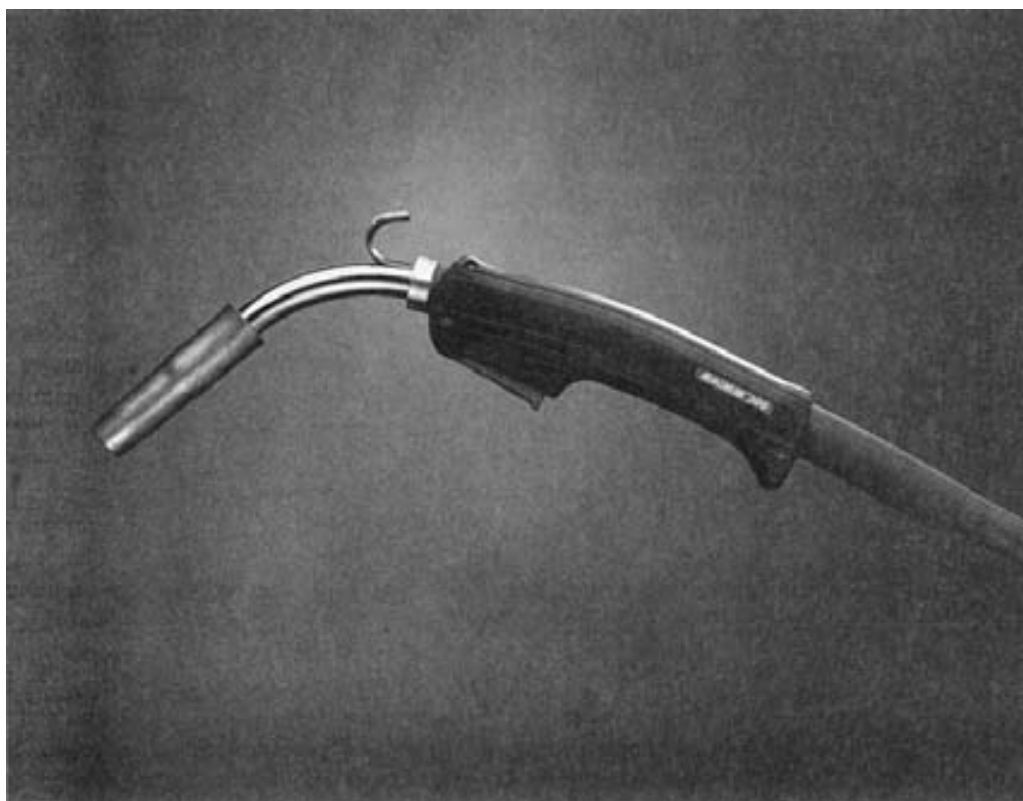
Pistola para soldadura con arco eléctrico de metal y gas. (Foto cortesía de Lincoln Electric Company).
